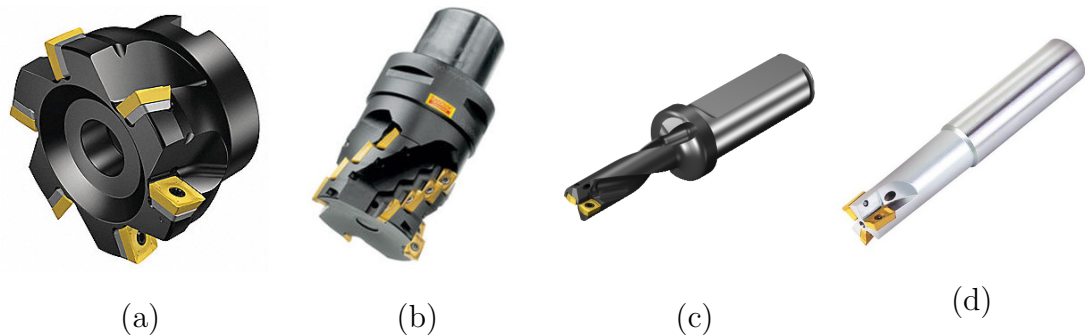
Fresa para planeado (a); desbaste (b); end mill (d) y broca (c)
